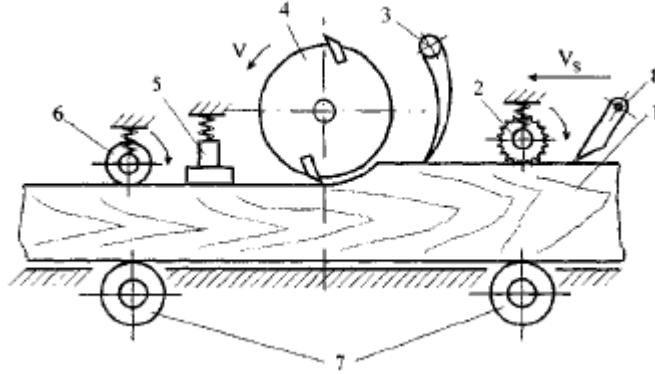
Функціональна схема рейсмусового верстата: 1 - заготовка; 2 - подаючий валець; 3 - притискач; 4 - ножовий вал; 5 - притискач; 6 - задній подаючий валець; 7 - непривідні вальці; 8 - противикидувач
